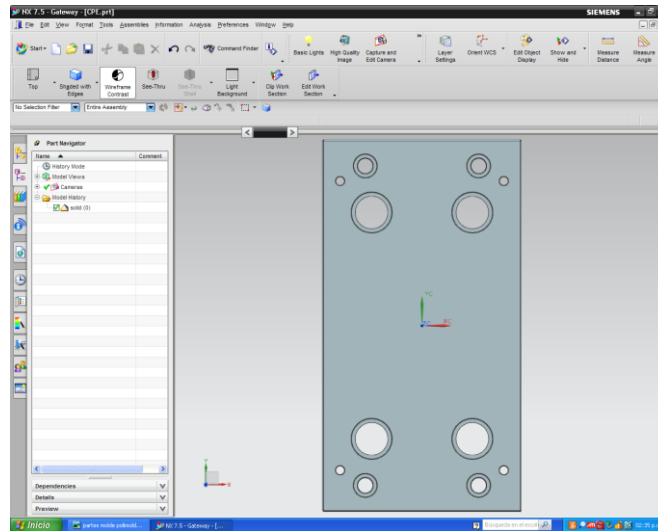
Placa limitadora de botadores CPE, vista frontal.
